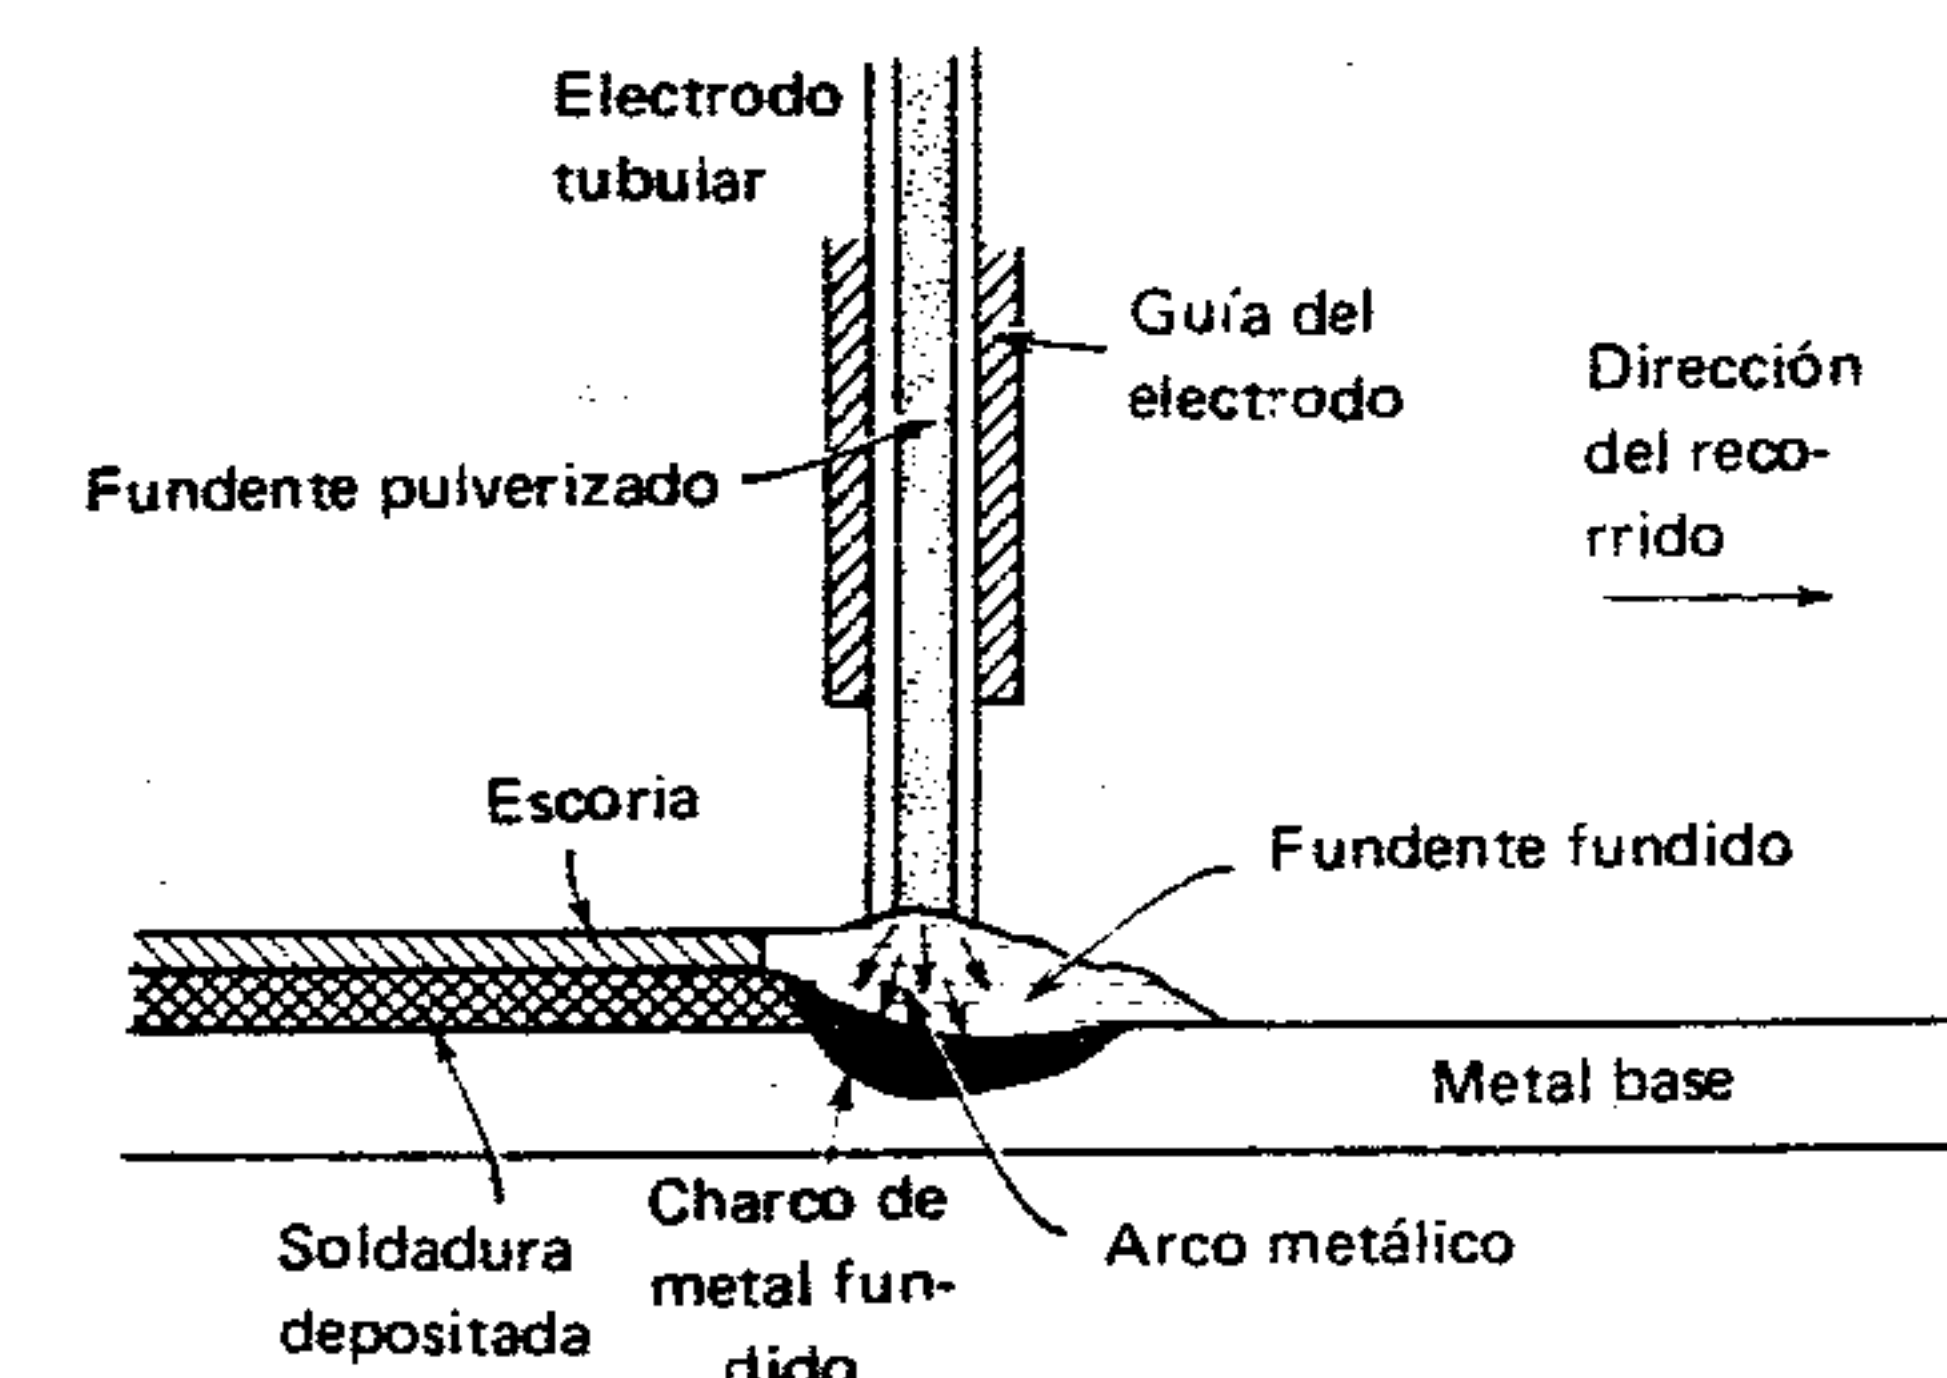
Soldadura de arco con alma fundente.
